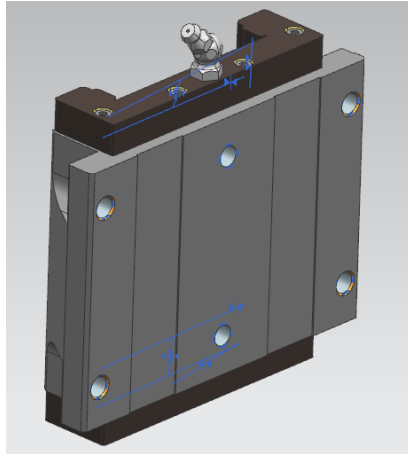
59. Carret de boles de la guia lineal KUVE25-WL.
